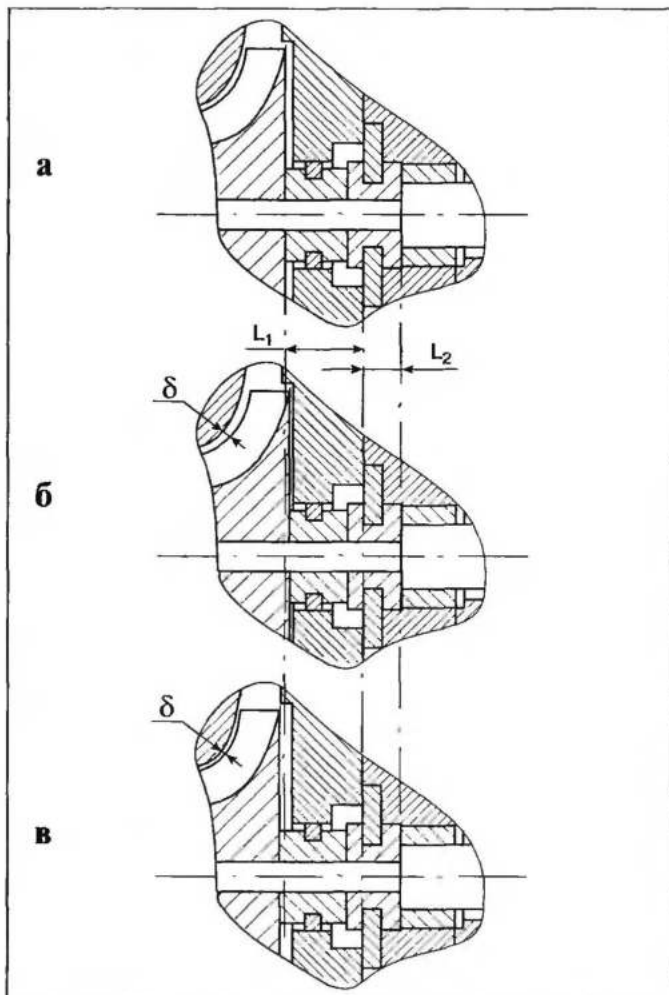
Влияние ширины деталей, устанавливаемых на роторе, на зазор между лопатками и корпусом (размер L_1 определяет положение колеса компрессора, L_2 - турбины): а — исходное состояние; б — ширина деталей уменьшена, зазор велик; в — ширина деталей увеличена, зазор мал
